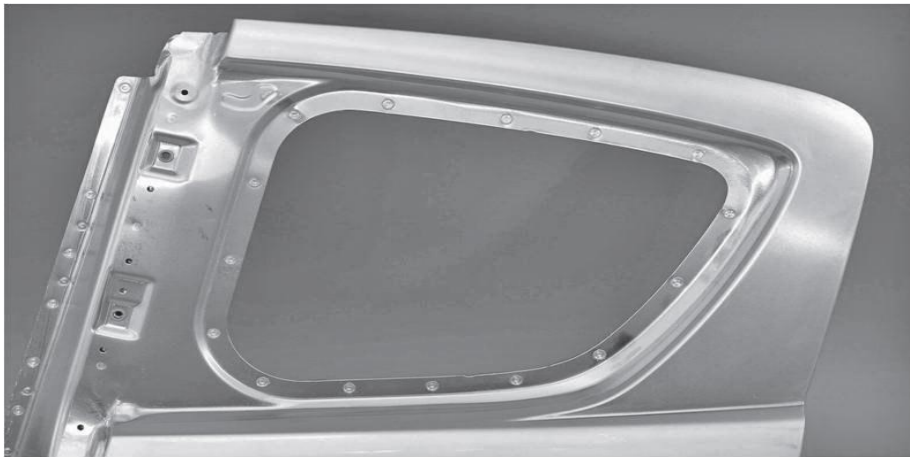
Porta traseira do Mazda RX8 soldada por FSW [11]
